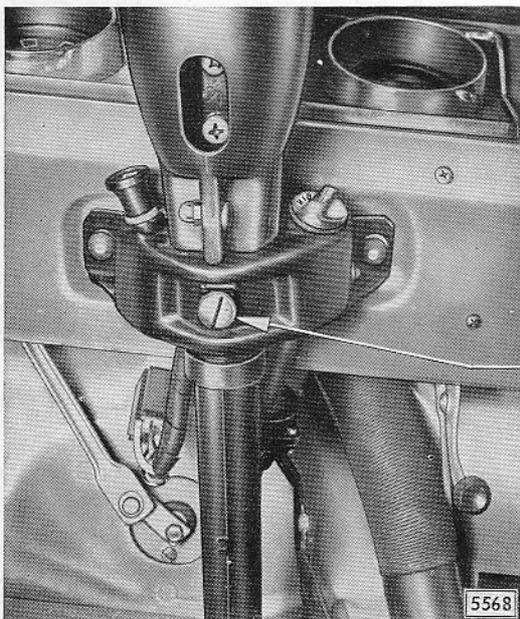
Anschlagschraube für Lenkspindel im Lenkstützrohrhalter
